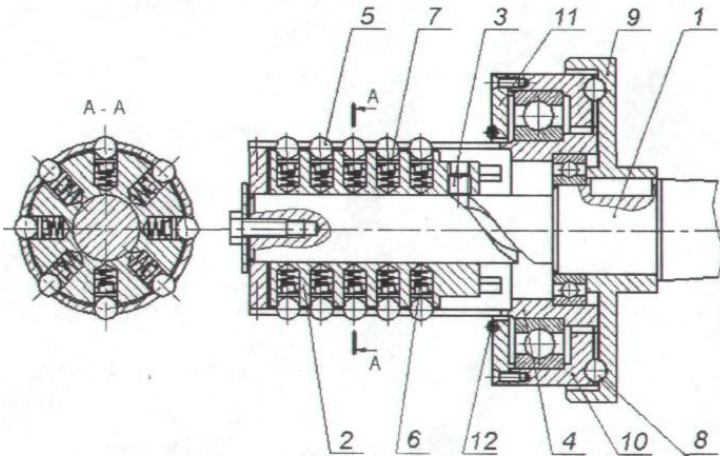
Конструкція багаторізного осцилюючого раскатника
